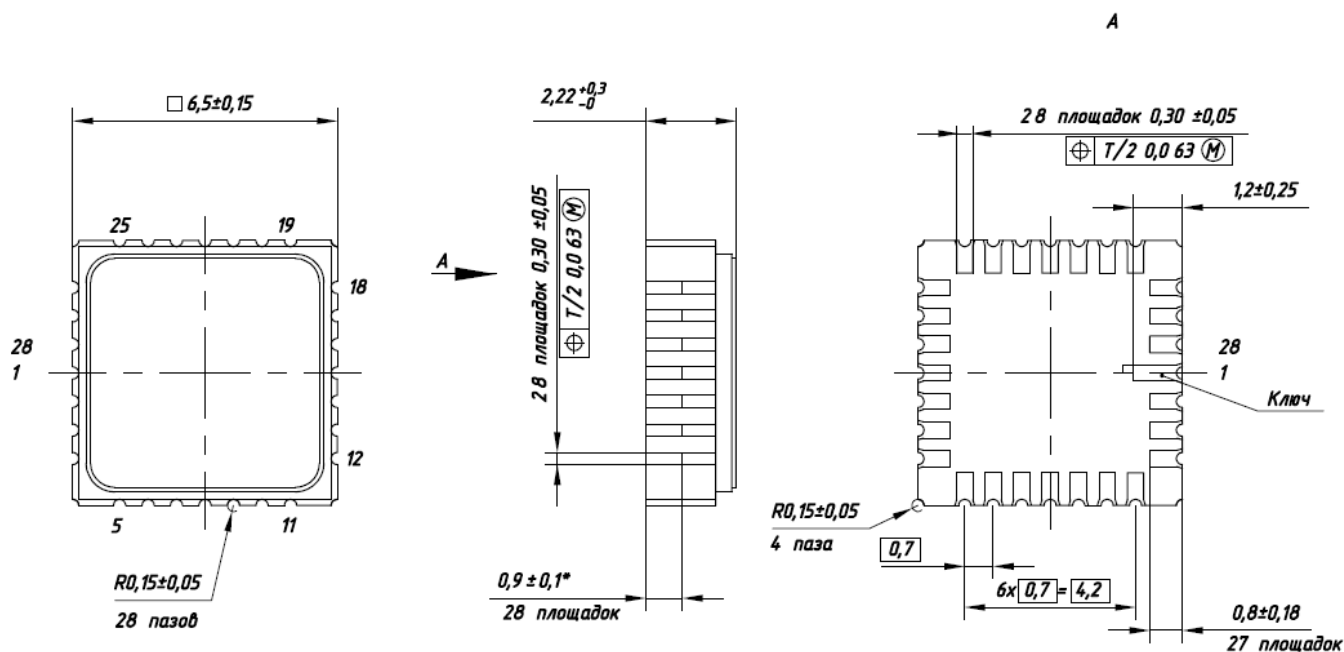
Габаритный чертёж микросхемы 1583HA065A в корпусе 5123.28-1.
